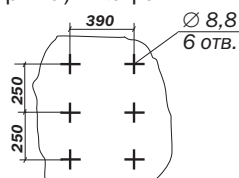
Установочные размеры шкафа ШРН-В/600
